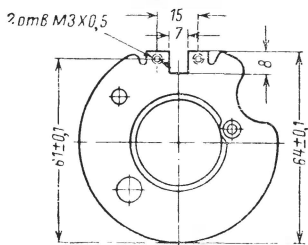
Чертеж доработанного подвижного диска прерывателя.
